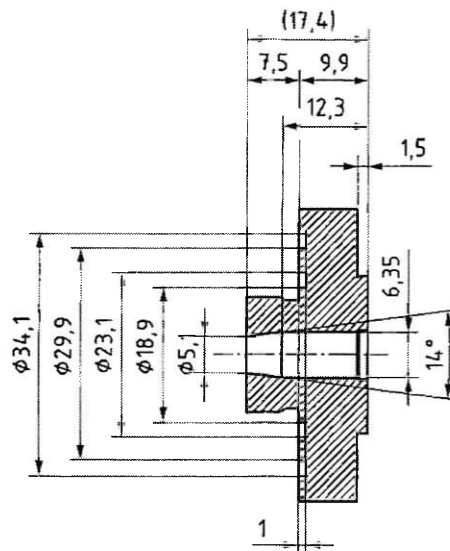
Insert de chambre à cartouche pour calibre 6,3/16
